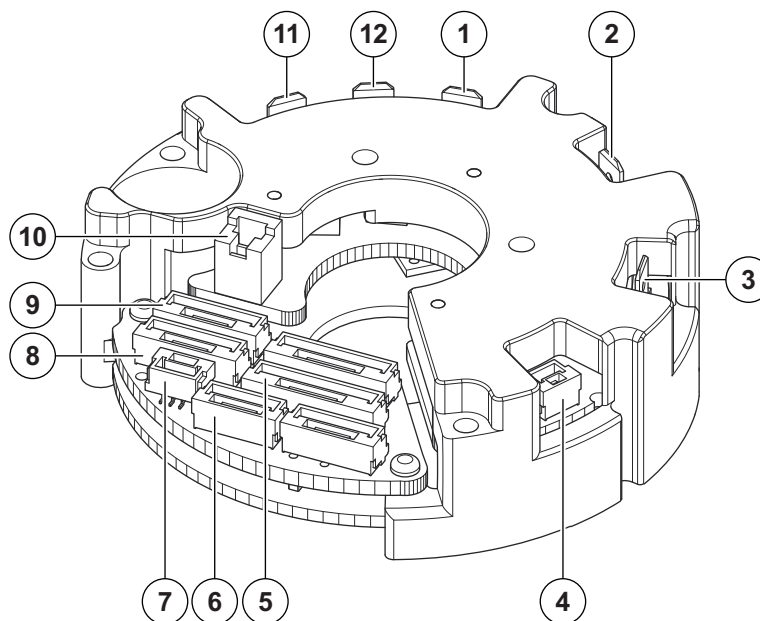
Anschlüsse TUAKE DRIVE (Beispielabbildung)
